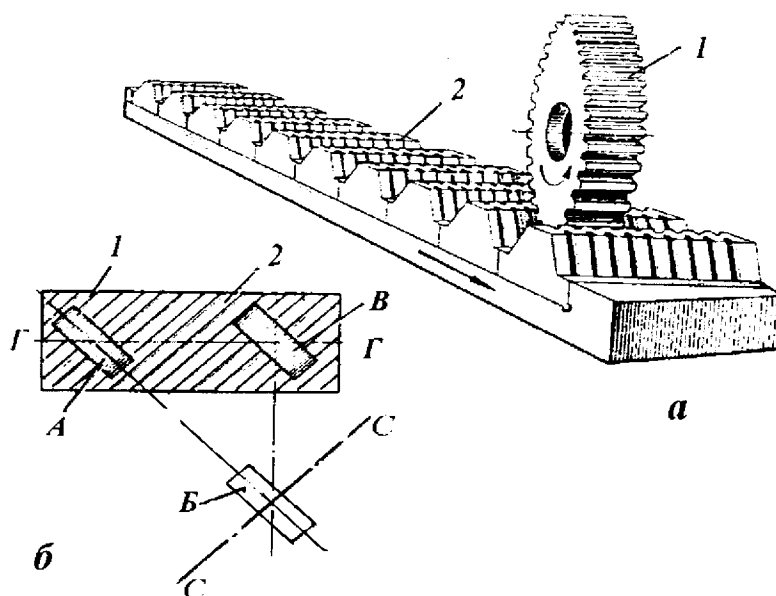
Шевингование шеввер-рейкой: *а* – шеввер-рейка; *б* – схема скольжения шеввер-рейки по зубьям зубчатого колеса.
